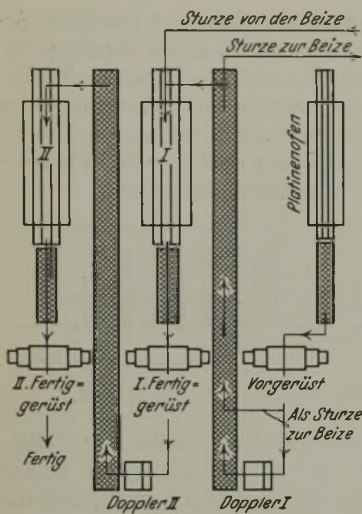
Straße mit zwei Fertigerüsten, das II. Fertigerüst getrennt für die zweite Fertigerisse und mit automatischen Platinen- und Blechöfen.
